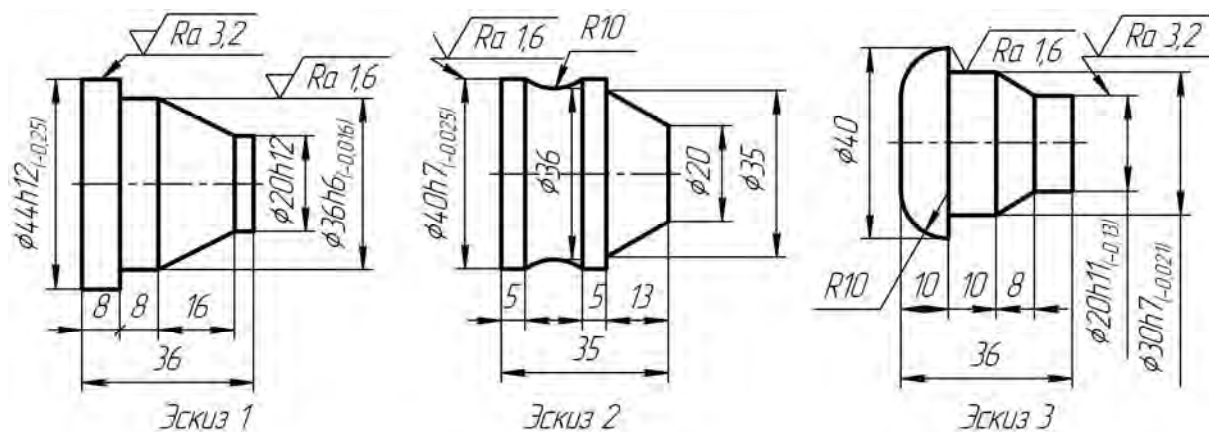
Эскизы деталей для расчета фасонных резцов
